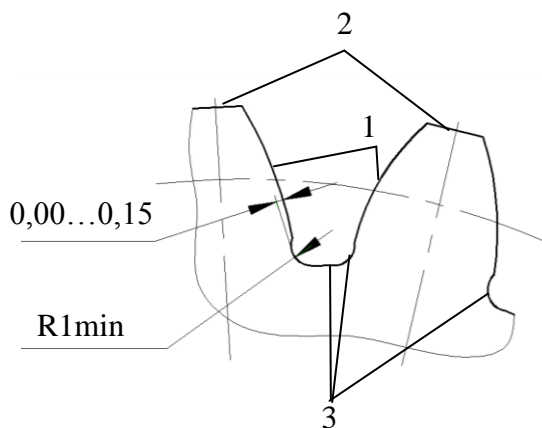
Цилиндрическое эвольвентное дисковое зубчатое колесо
